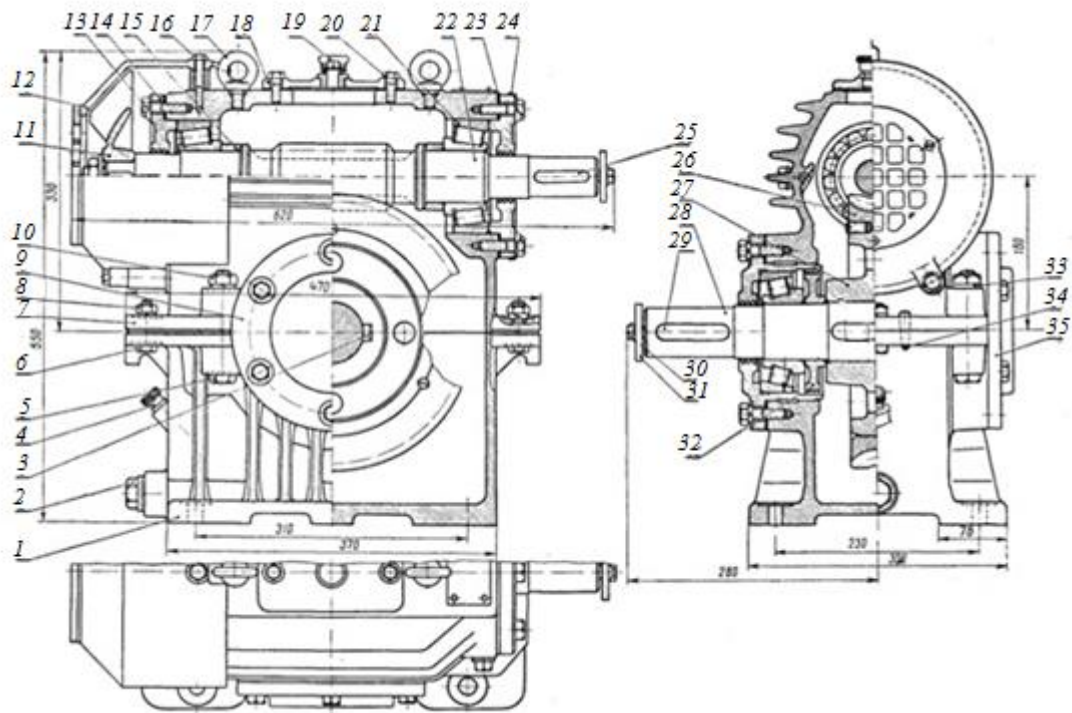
Редуктор черв'ячний з верхнім розташуванням черв'яка:
